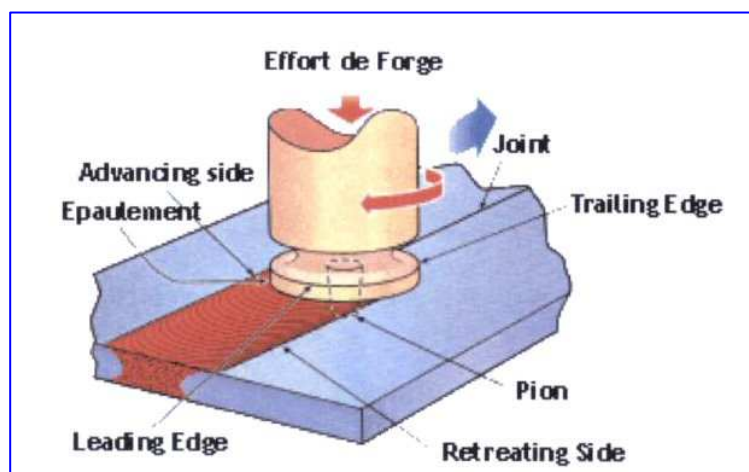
Principe de la technique "Friction Stir Welding".
